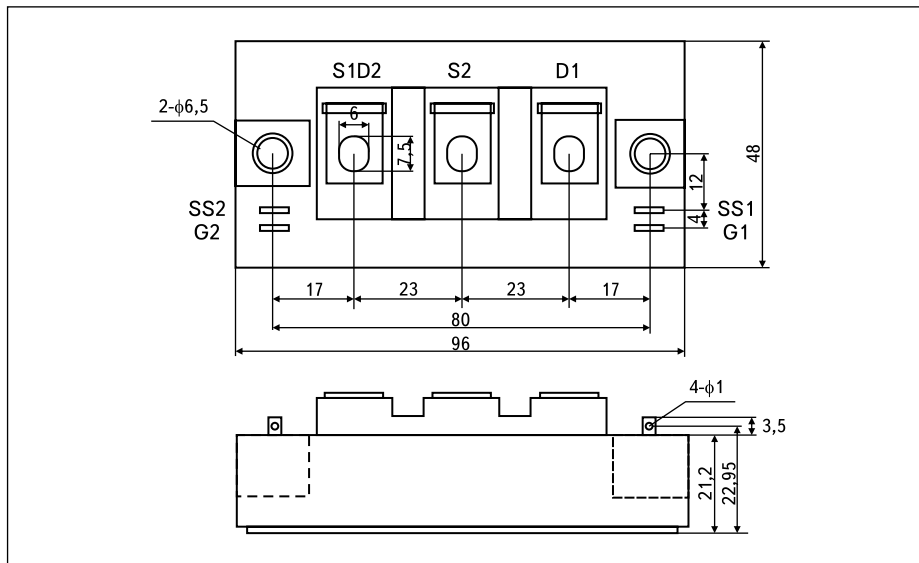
Габаритный чертеж силового модуля на основе SiC
